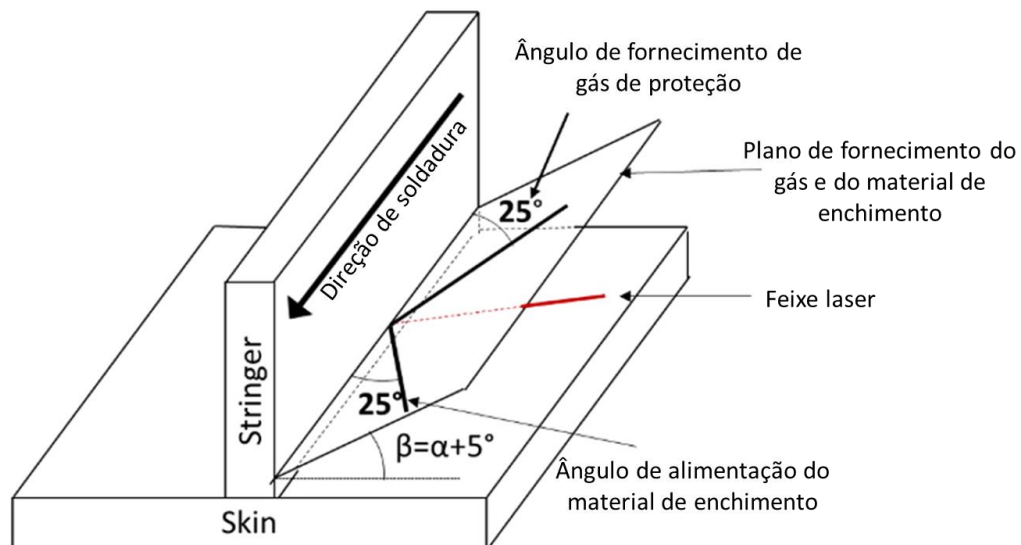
Adição de material e de gás de proteção relativamente ao cordão de soldadura
